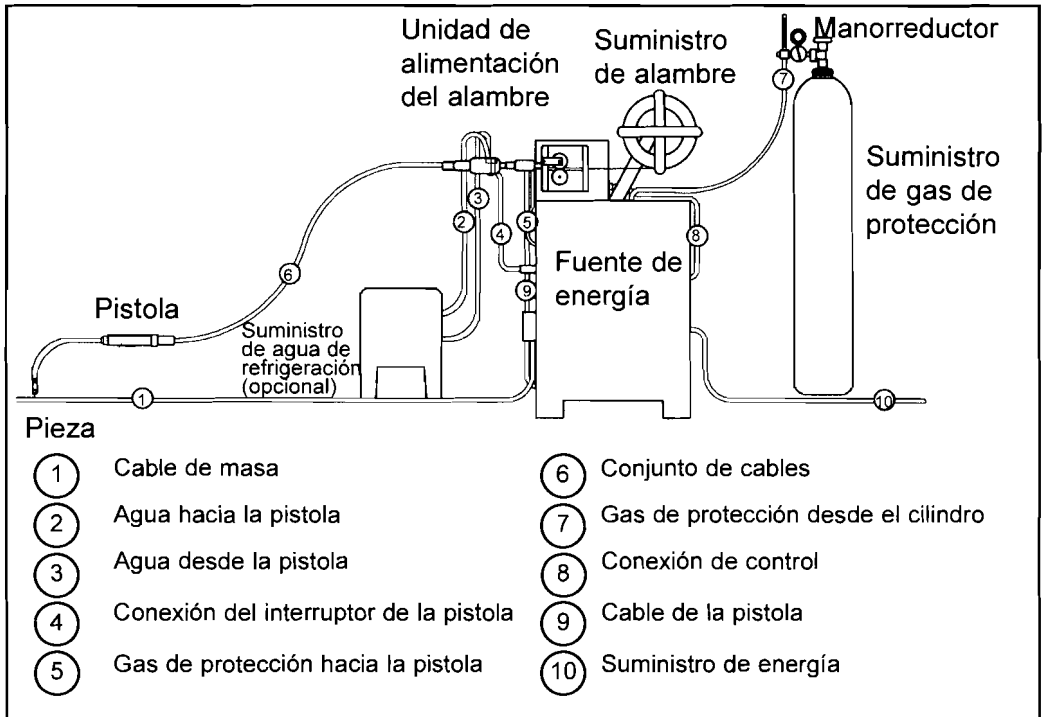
EQUIPO PARA EL SOLDEO MIG/MAG
